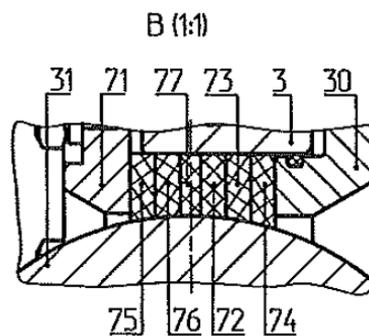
Расположение кольца уплотнительного поз. 75 сферического уплотнения поворотного шарнира
